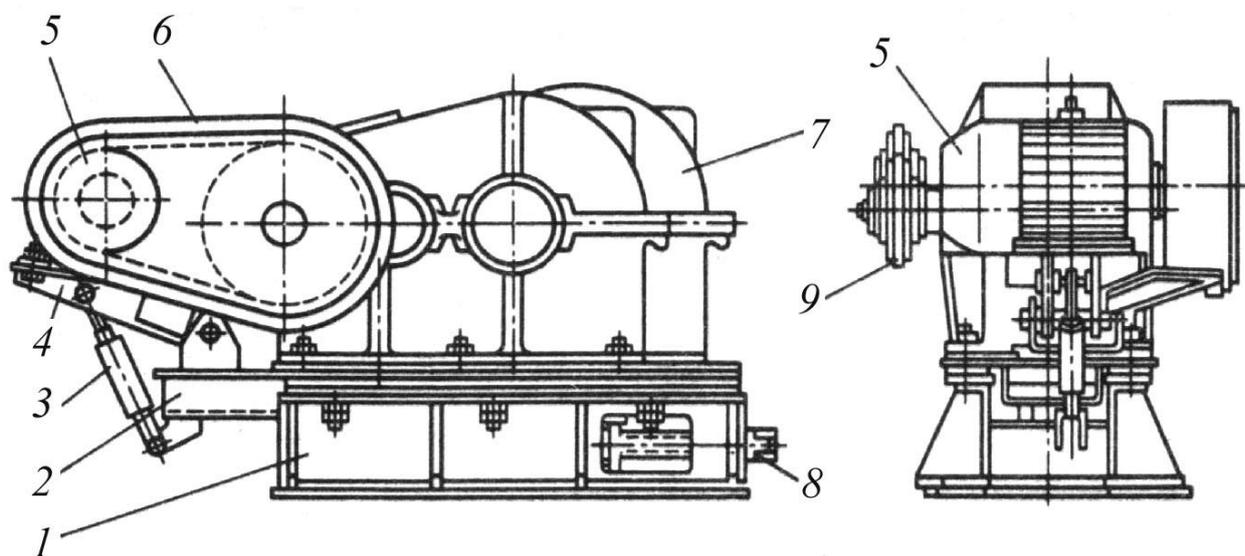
Привод транспортера конструкции ВНИИПТМАШа.
